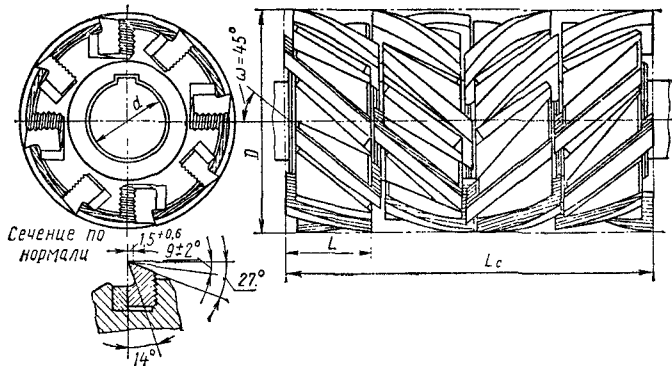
Цилиндрическая фреза со вставными зубьями с углом  $\omega = 45^\circ$  (конструкция завода «Фрезер»)
